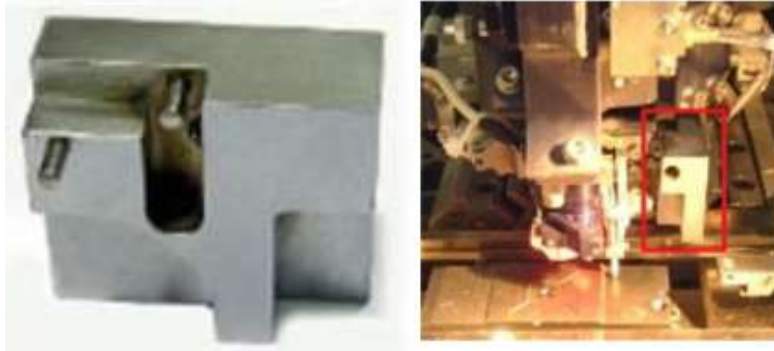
Calibrador de fuerza y montaje en equipo. [17]
